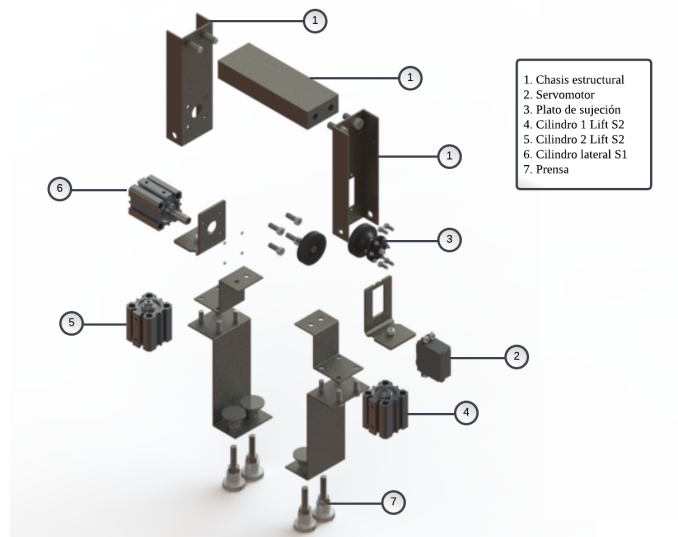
Vista Explosionada del Mecanismo. Fuente: Autores
